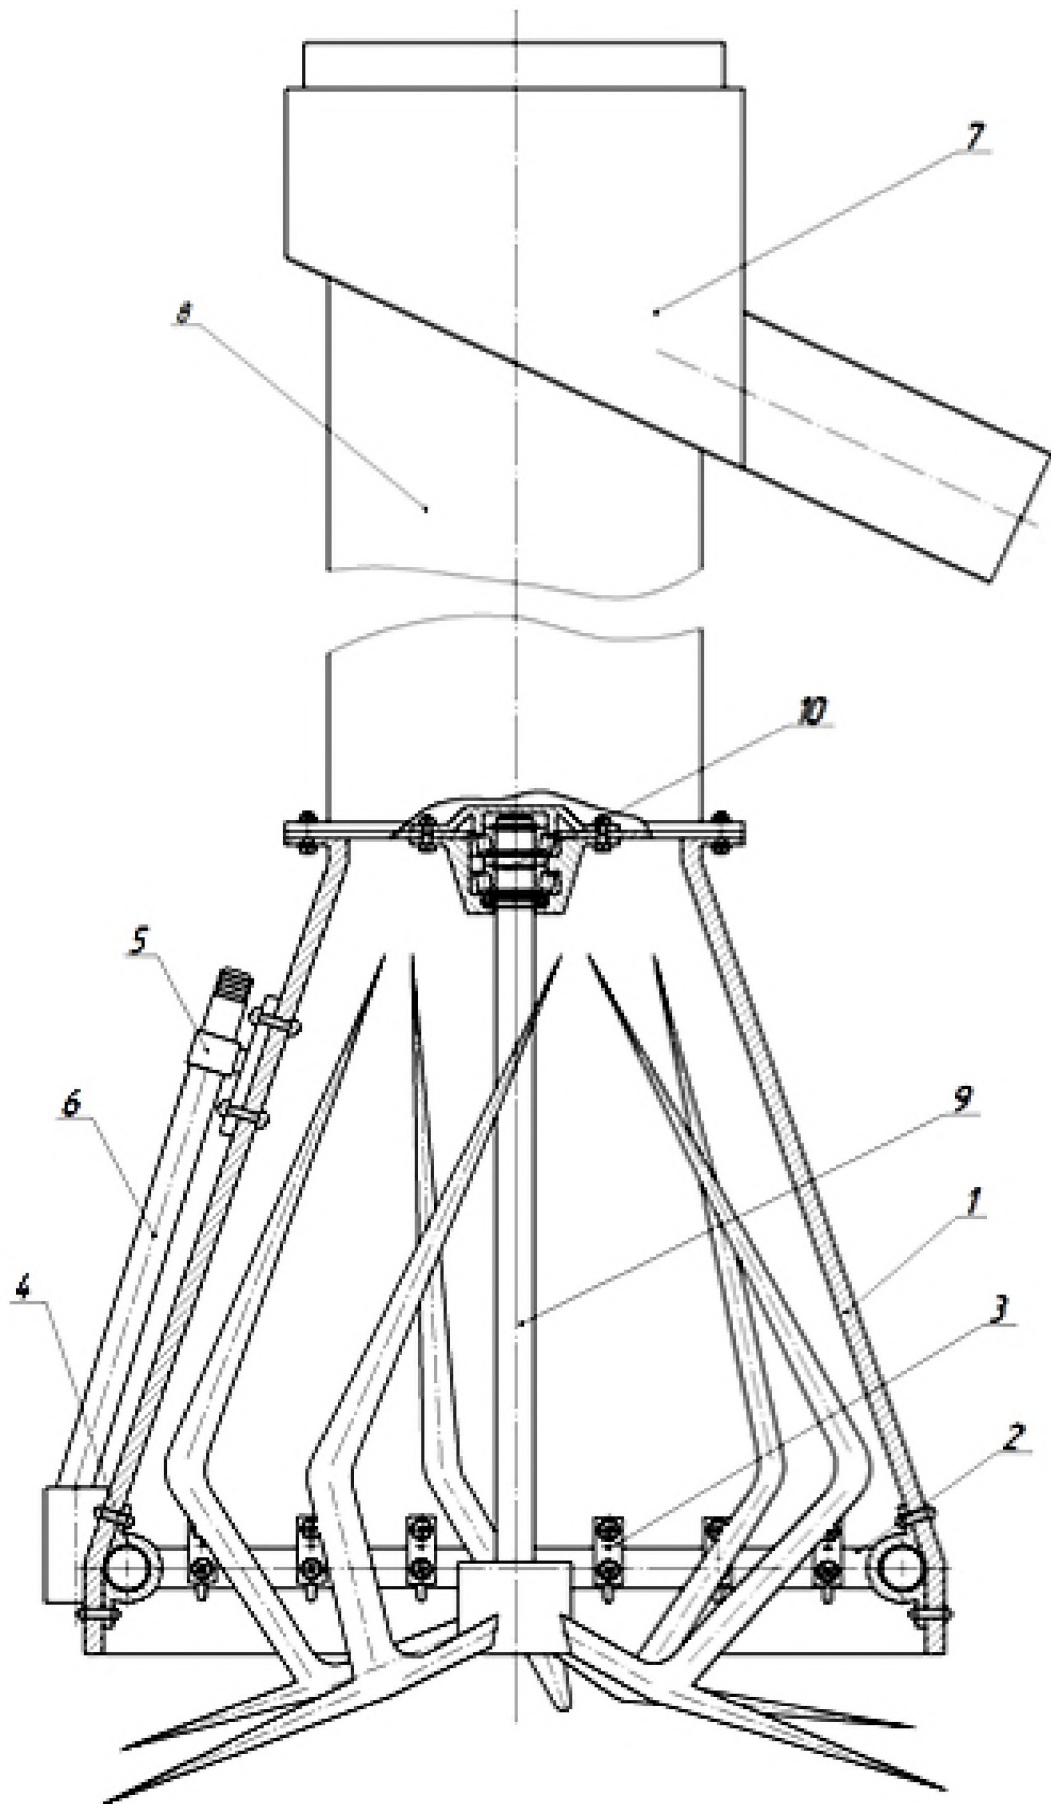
Схема пневмомеханічного забірного пристрою: 1 – змішувач; 2 – напірна порожнина; 3 – форсунки зборі; 4, 5 – кронштейни; 6 –
